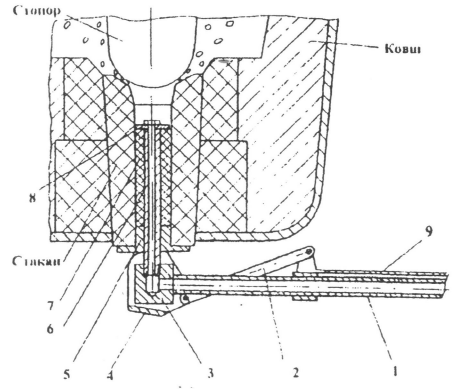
Схема устройства для продувки стали газом в стопорном разливочном ковше.
